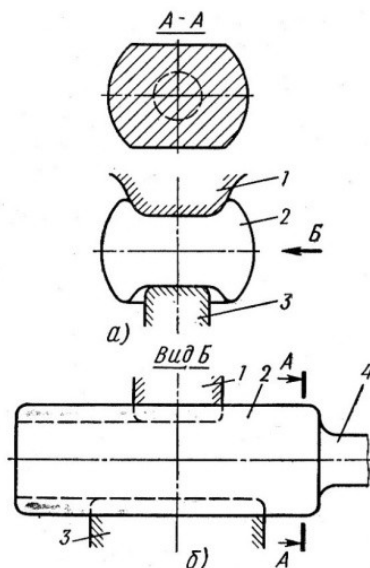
Спосіб заварки внутрішніх пустот підстуженого зливка: а – сбілетований злиток після утворення на ньому поздовжніх лисок; б – обтиснення вузькими бойками для зварювання пустот; 1 – верхній вузький та короткий боек; 2 – обтискає мий підстужений біллет; 3 – нижній, вузький, більш довгий боек; 4 – цапфа під патрон
